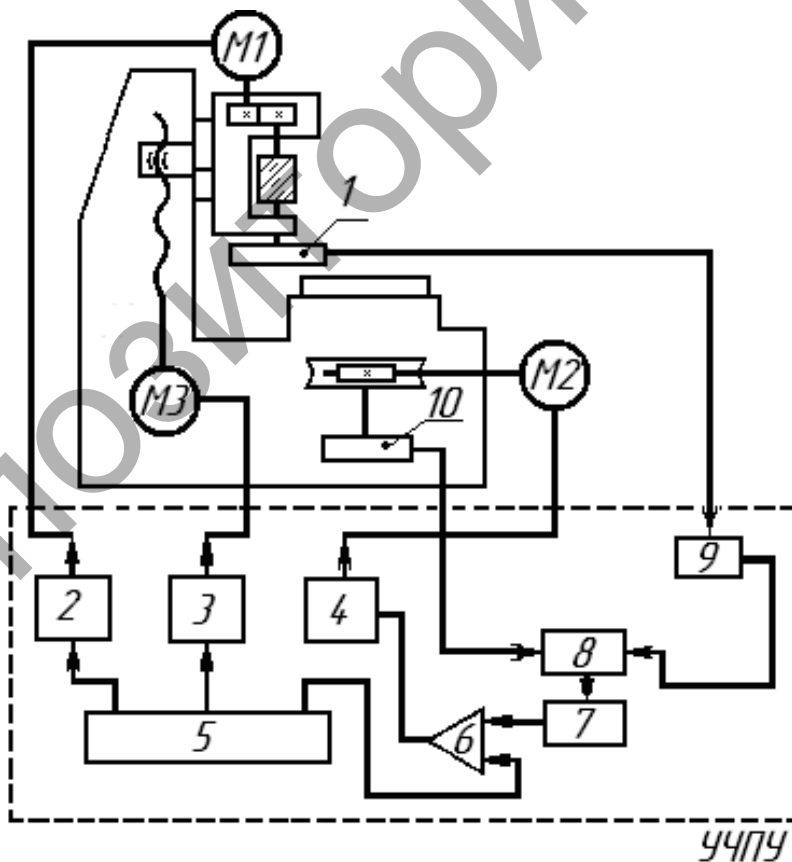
Структурная схема зубофрезерного станка с ЧПУ
